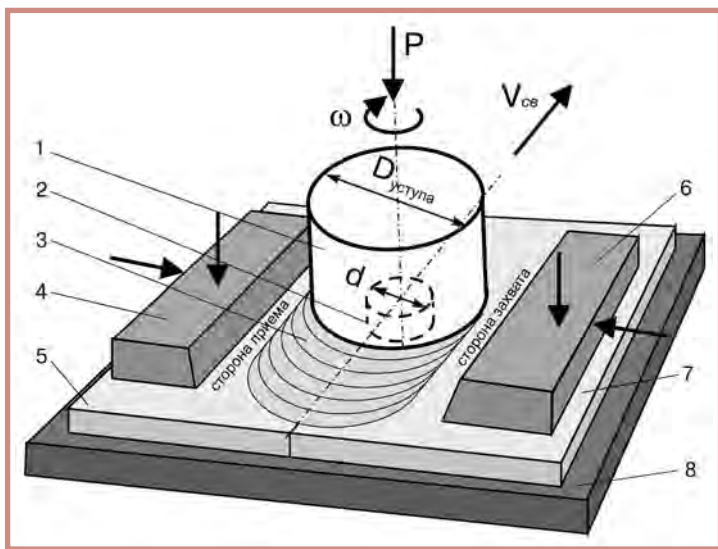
Схема выполнения СТП: 1 — сварочный инструмент; 2 — наконечник сварочного инструмента; 3 — сварной шов; 4, 6 — прижимные планки; 5, 7 — свариваемые заготовки; 8 — технологическая подкладка ( $\omega$  — скорость вращения сварочного инструмента;  $V_{св}$  — скорость сварки;  $D_{уст}$  — диаметр опорной поверхности уступа сварочного инструмента;  $P$  — осевое давление сварочного инструмента на свариваемые заготовки)
